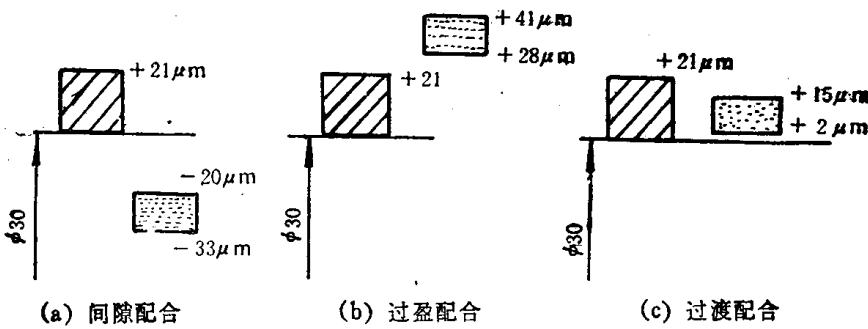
例2-2、2-3、2-4的公差带图
